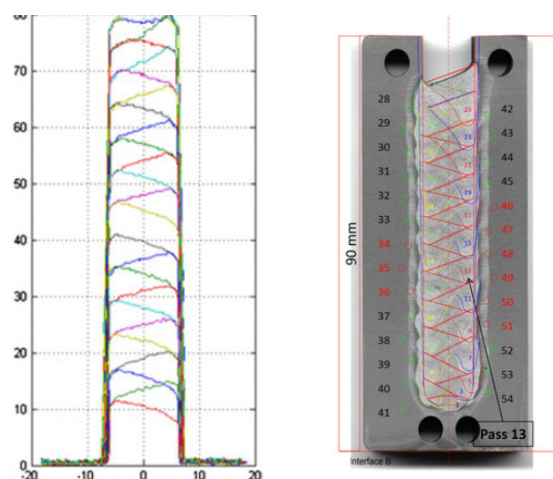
Cumul des profils scannés après chaque passe de soudage; Superposition sur la macrographie réelle de la position des thermocouples, des sections des cordons et des profils de chaque passe de soudage [2].
